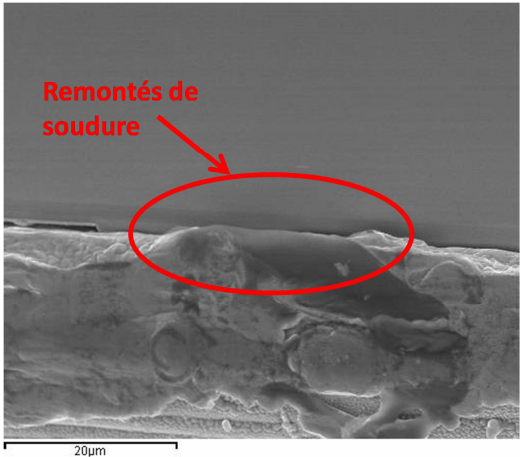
Photo MEB de la facette de sortie d'un laser large dont la soudure a partiellement occulté la zone active
